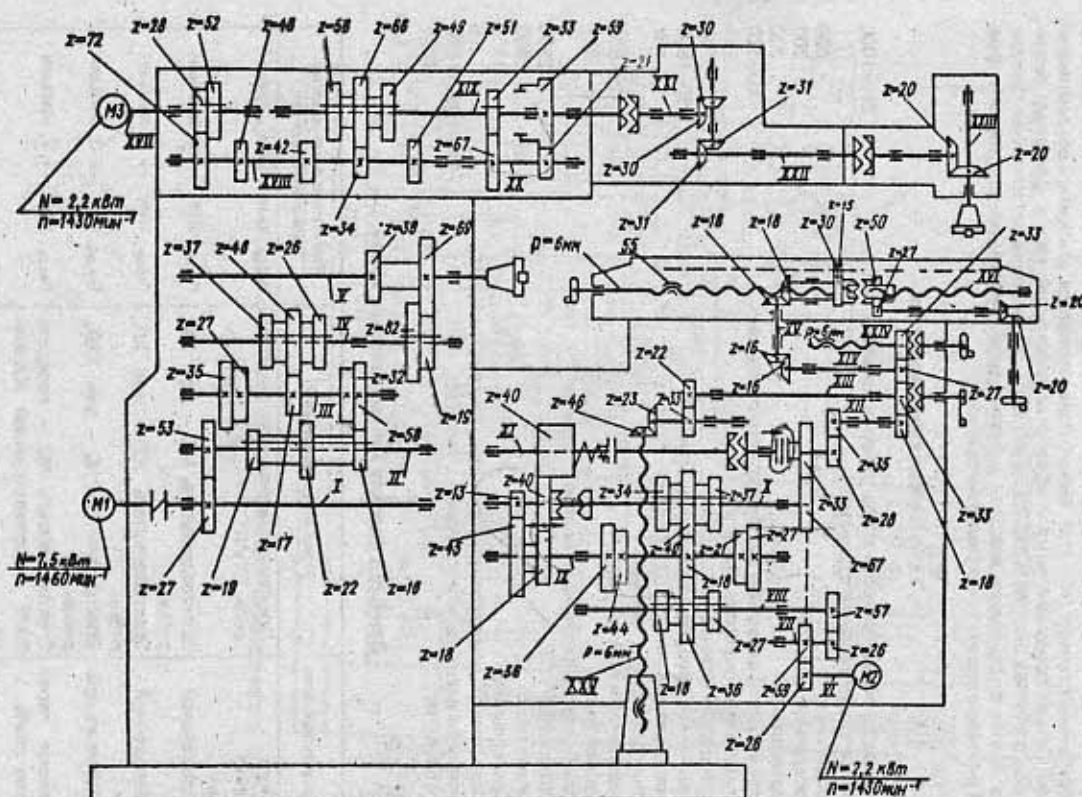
Кинематическая схема широкоуниверсального фрезерного станка мод. 6Р82Ш
